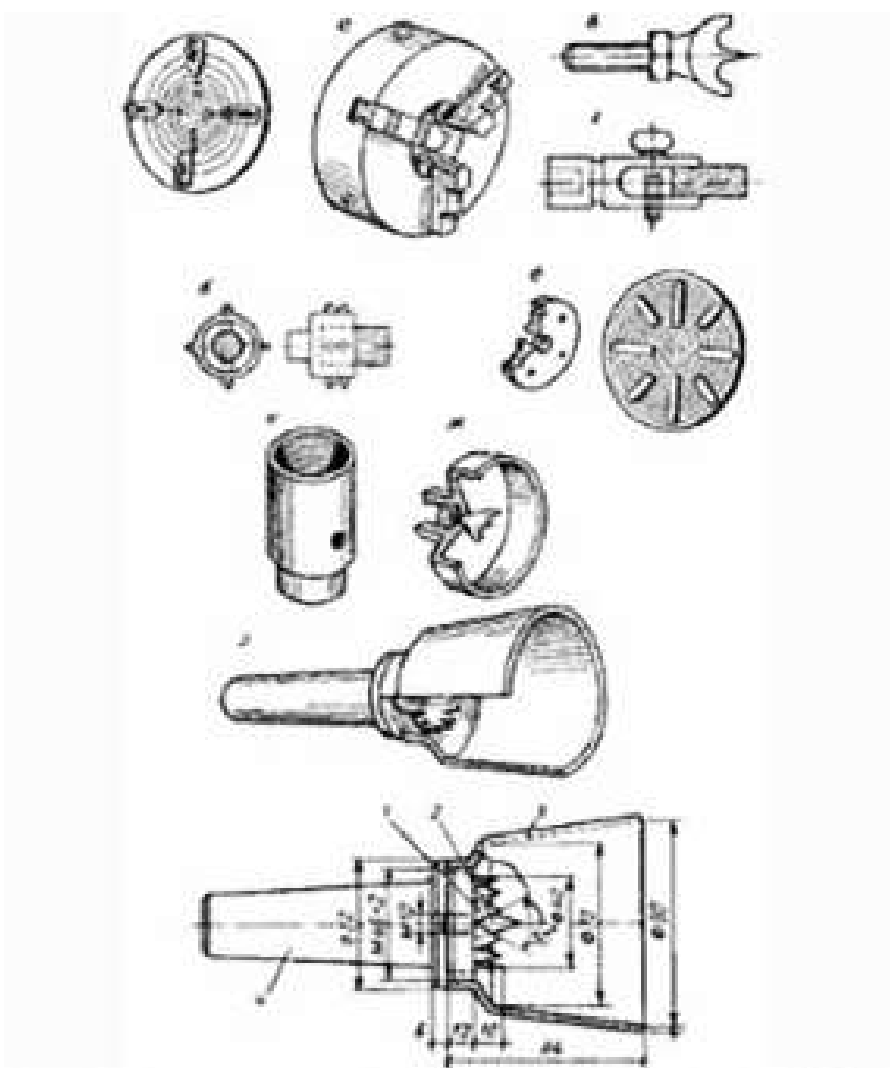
Пристосування для закріплення і обробки заготовок на токарному верстаті СТД120М
